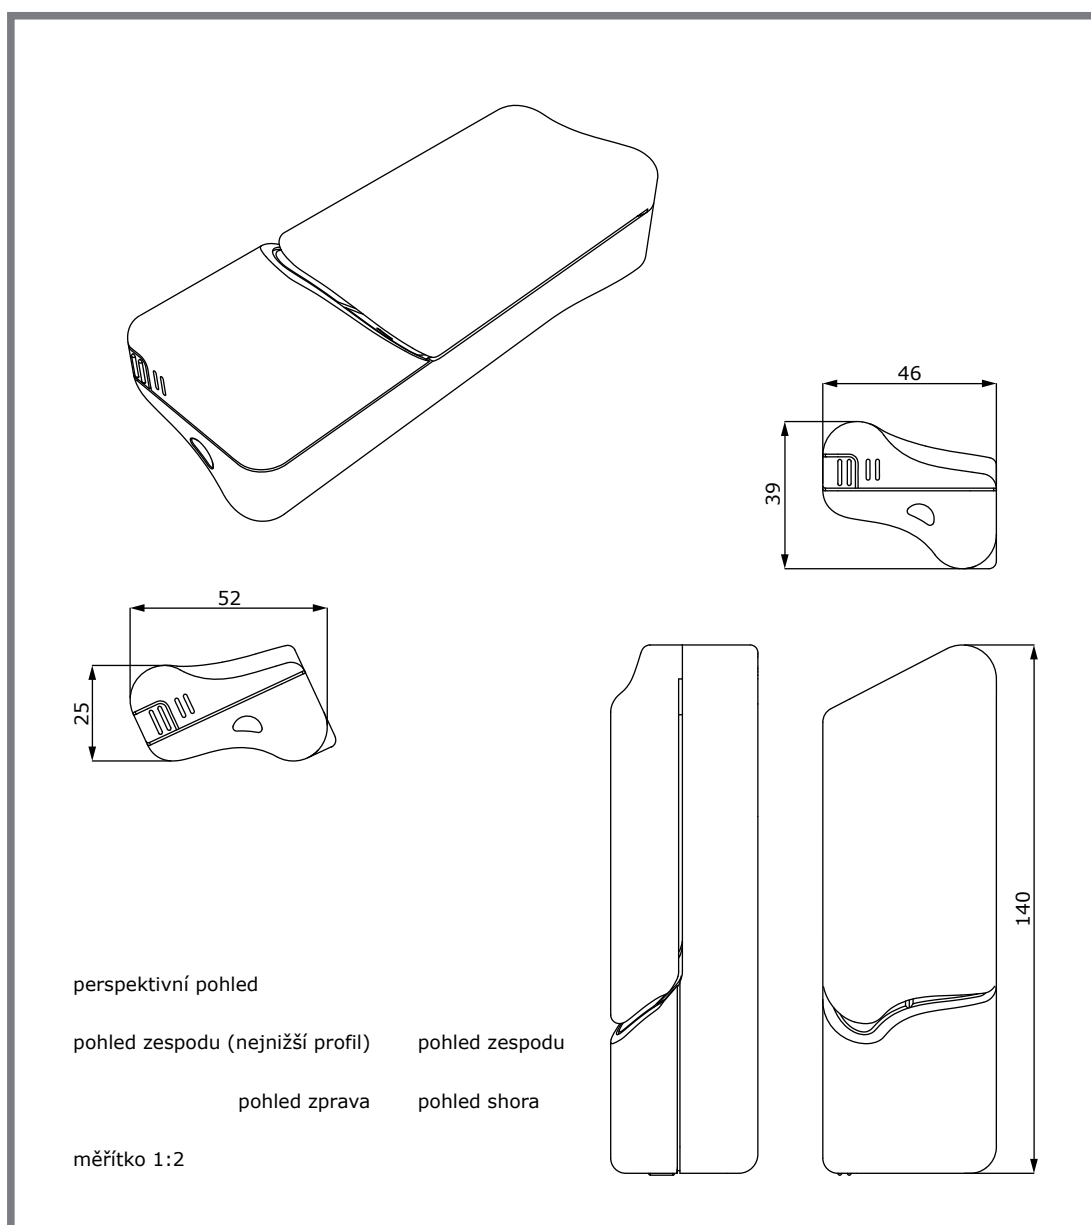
Detail krytu konektoru a reproduktoru, autor
